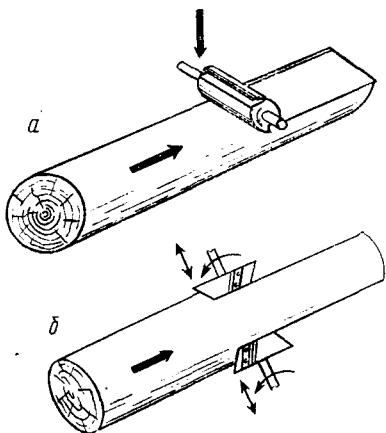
Фрезерная установка для производства шпал и брусьев: а — фрезерного типа; б — дискового типа
